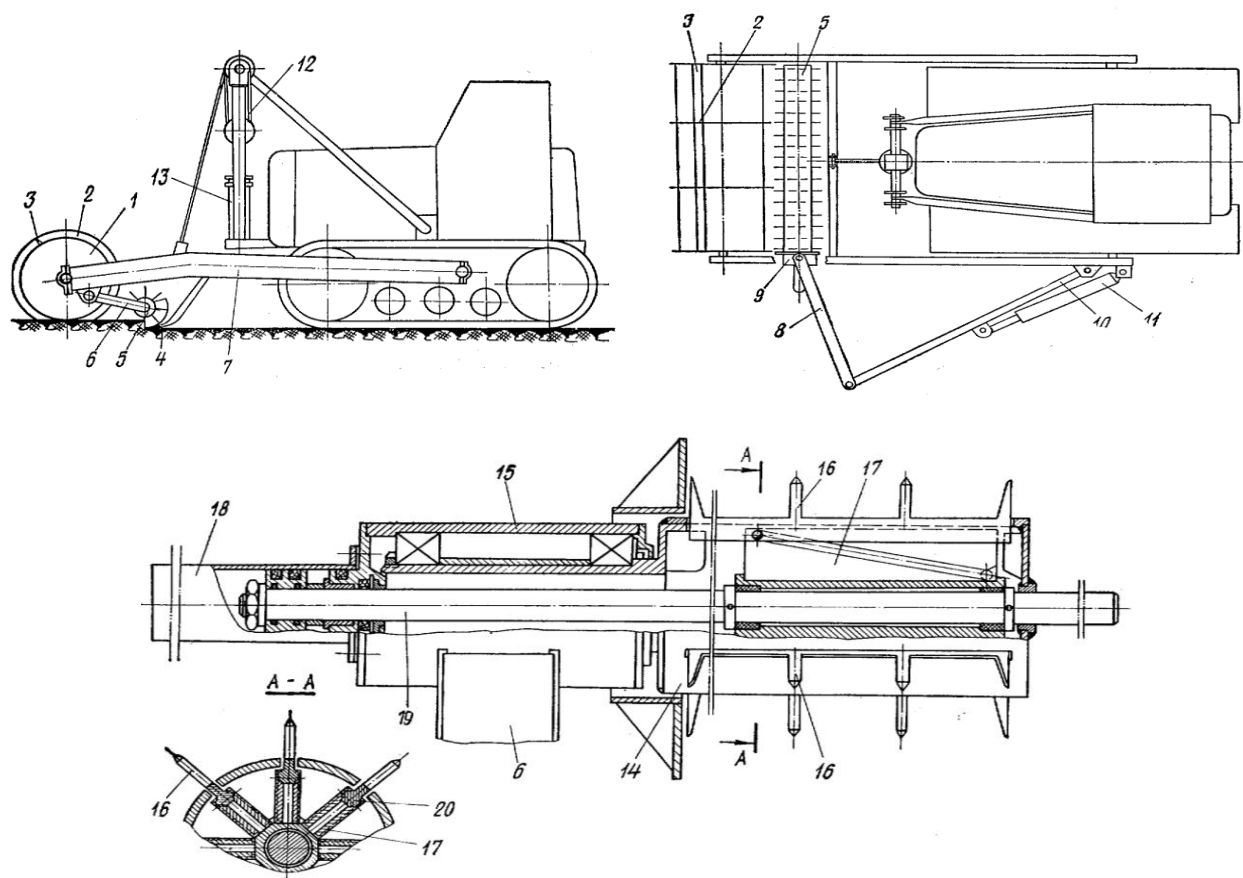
Устройство для свертывания дерновых лент в рулоны
